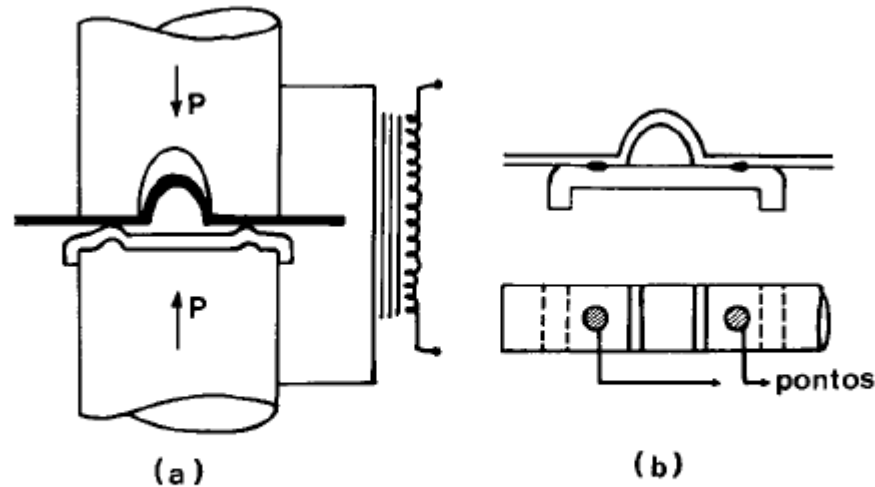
Esquema do processo de soldagem por ressalto (a) mostrando o tipo de soldagem obtida (b)
